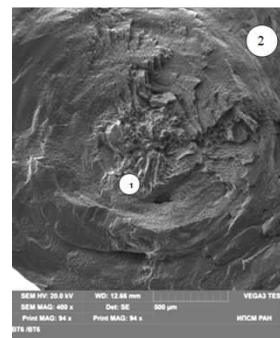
Внешний вид излома сварного соединения ВТ6/ВТ6
